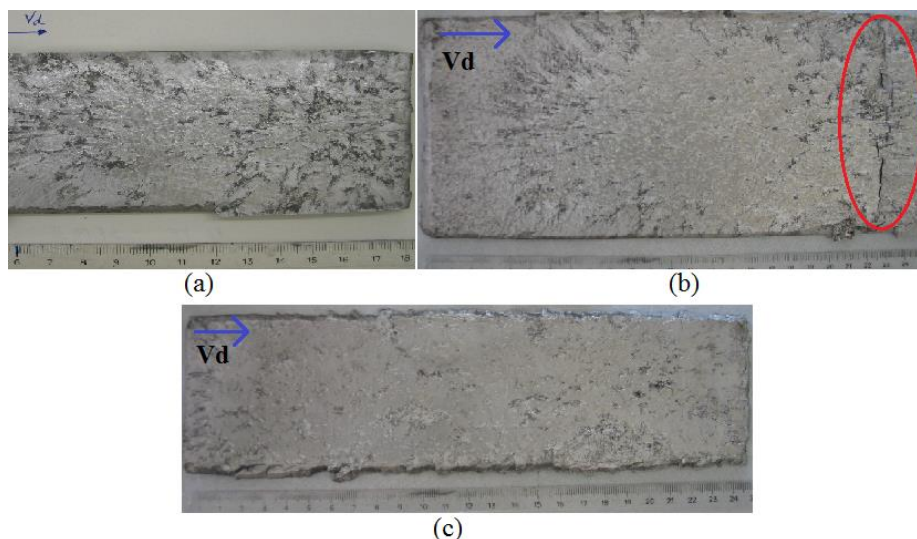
Efeito do Rácio na superfície final da soldadura: (a) superfície exterior da EW 15-Al.Fe-5.3; (b) superfície exterior da UEW 20-Al.Fe-5.3; (c) superfície exterior da UEW 21-Al.Fe-5.3.
